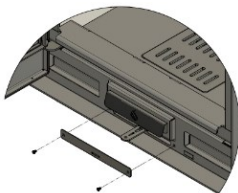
Retire los tornillos; coloque la pieza de sellado y vuelva a apretar los tornillos.
